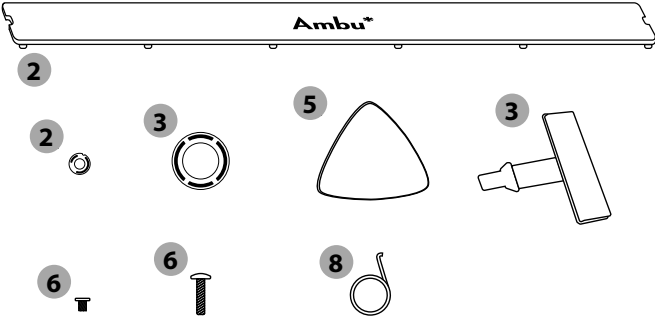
Instalar a tampa se a placa VDI tiver sido removida
